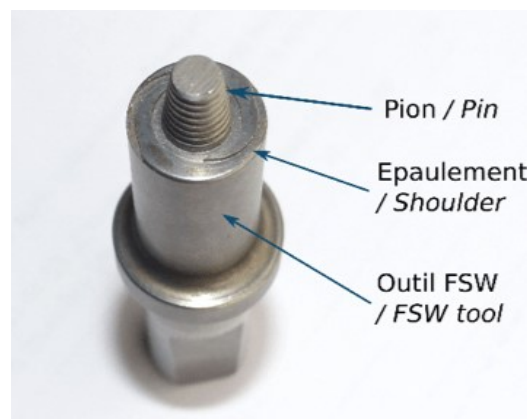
Componenti principali di un utensile utilizzato per il processo di FSW [7].
